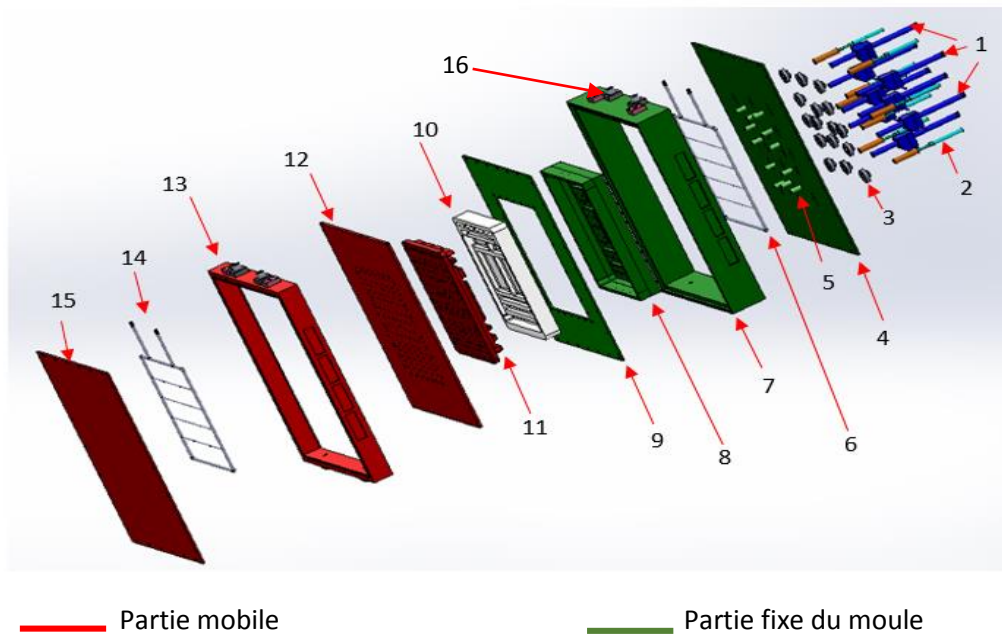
Partie mobile du moule en 3D conçu par SolidWorks.
